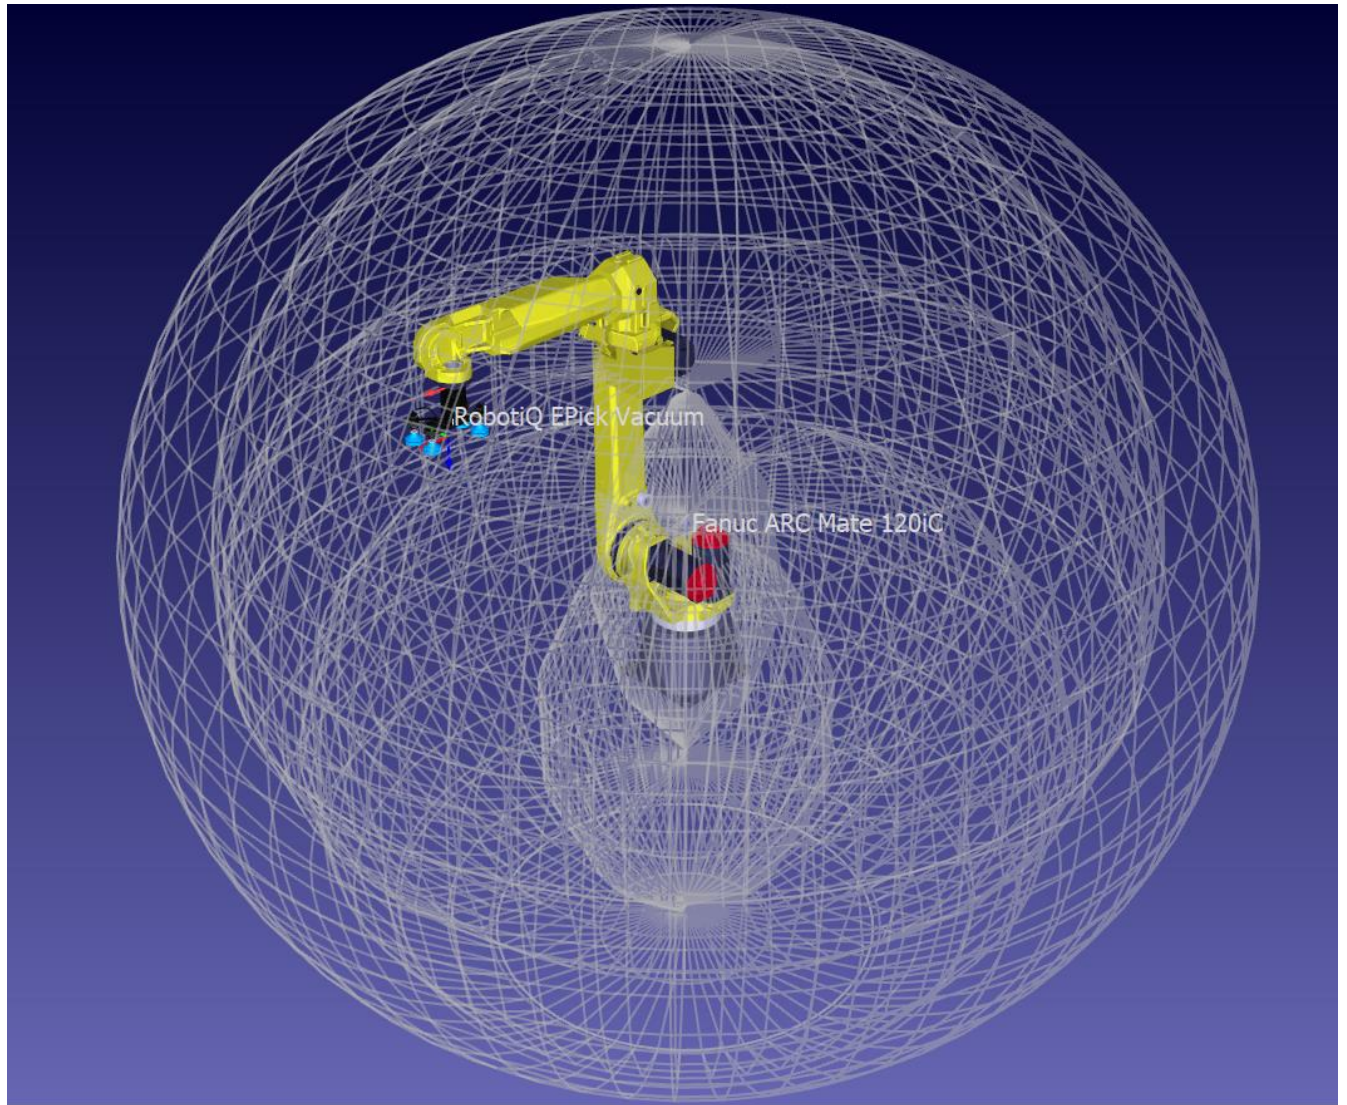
Робоча зона робота з пневматичними захватами
